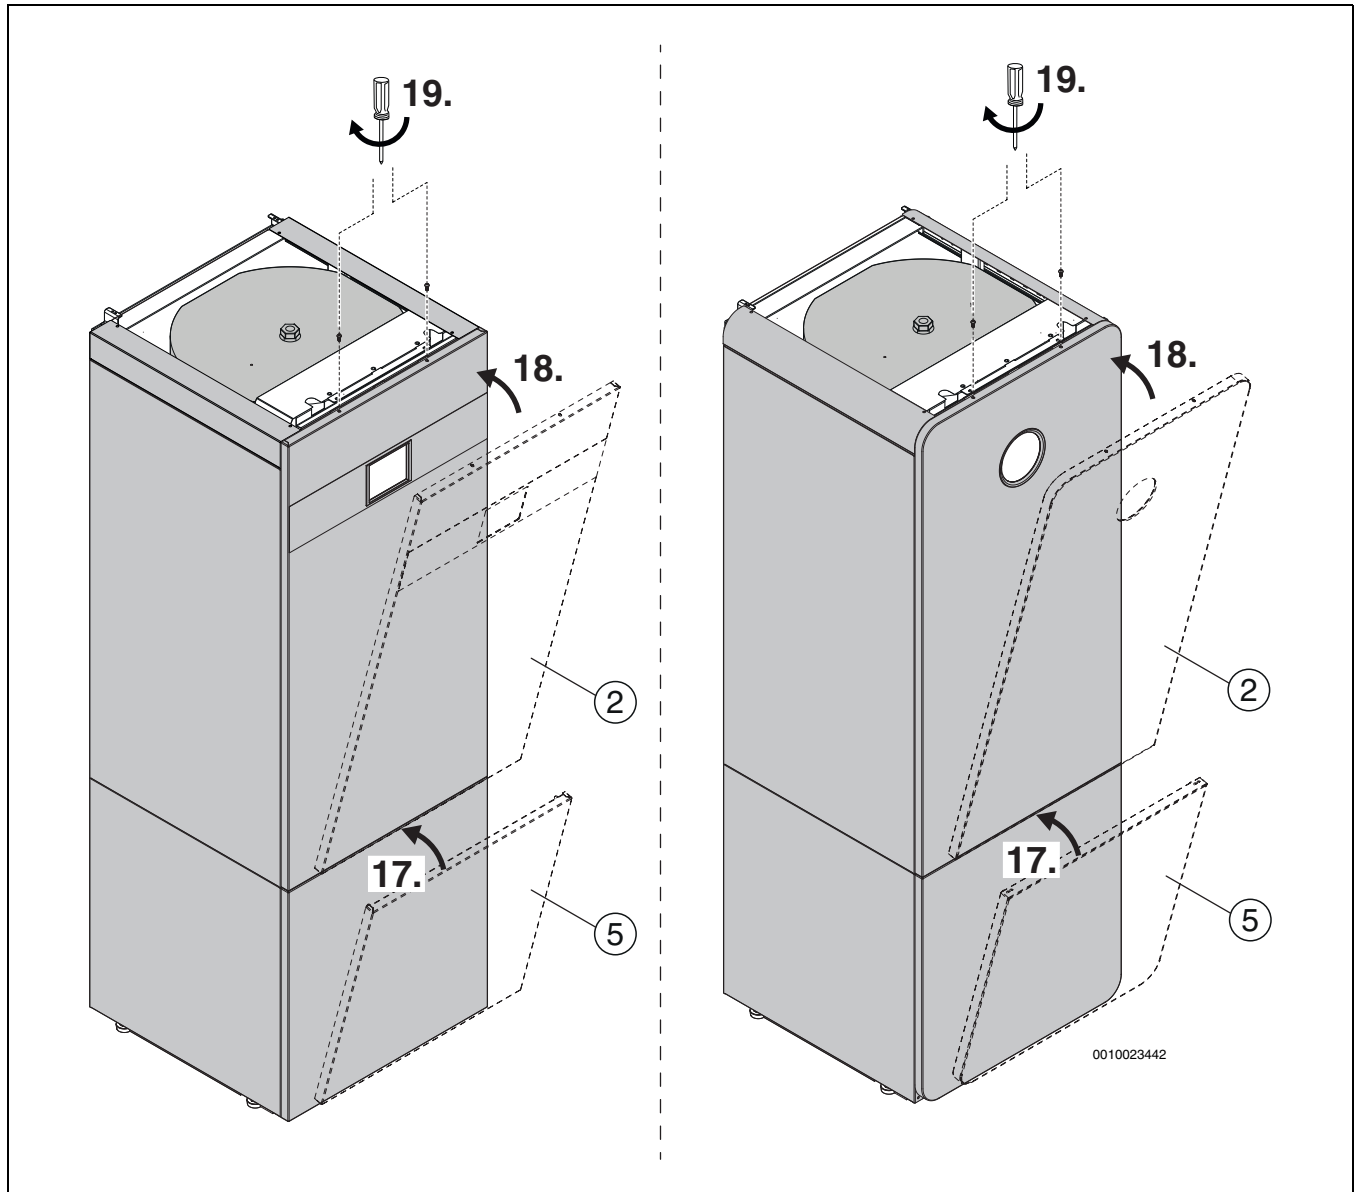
Montering af forvægge med firkantet eller rund afdækning
